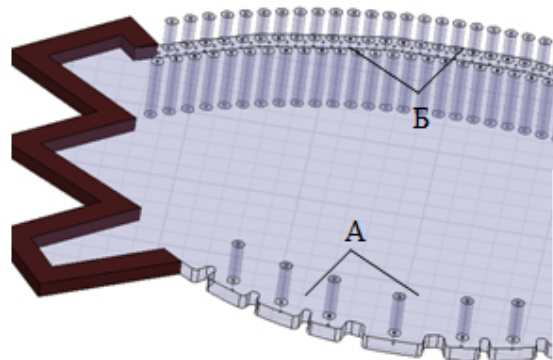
(А – металлический корпус с выфрезерованной полостью, В – металлическая крышка)
